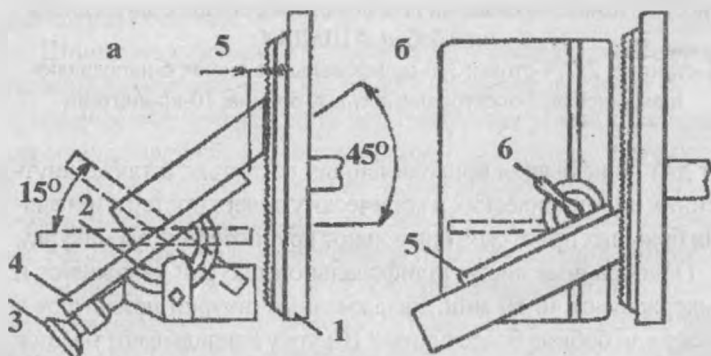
Наладка комбинированного шлифовального станка: а-настройка стола; б-регулировка направляющей линейки; 1-диск; 2-направляющие; 3-маховичок; 4-стол; 5-линейка; 6-зажим
